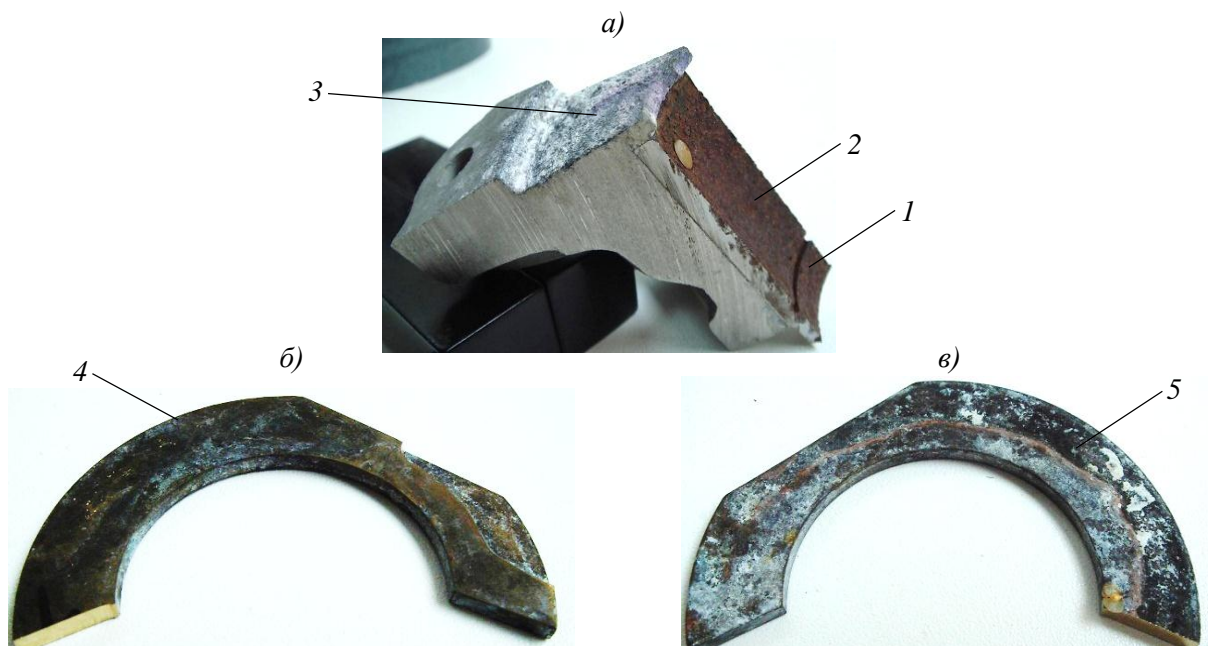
Внешний вид сегмента корпуса маслонасоса (а), верхняя (б) и нижняя (в) поверхности втулки из бронзы БрАЖН-10 с областями проточки (1) на обойме из стали типа 30Х3МФ (2) и посадочным местом (3) в корпусе из сплава АК7ч. под втулку из бронзы БрАЖН-10, а также верхняя (4) и нижняя (контактная с корпусом маслонасоса) поверхности (5)
